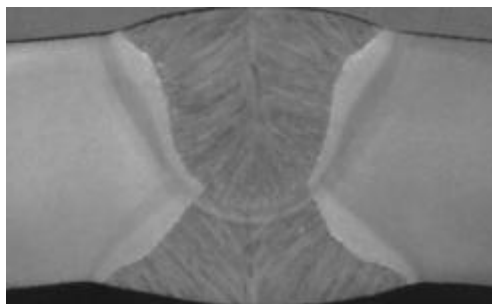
Φ1 016 mm×21.0 mm 焊管焊缝宏观形貌
